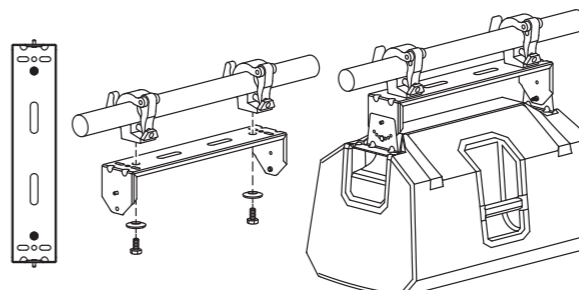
Horizontale Montage mit TCA-1 Traversenklemmen
